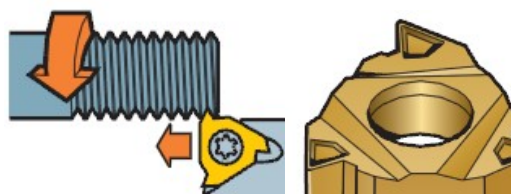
Інструмент для нарізання зовнішньої різьби
